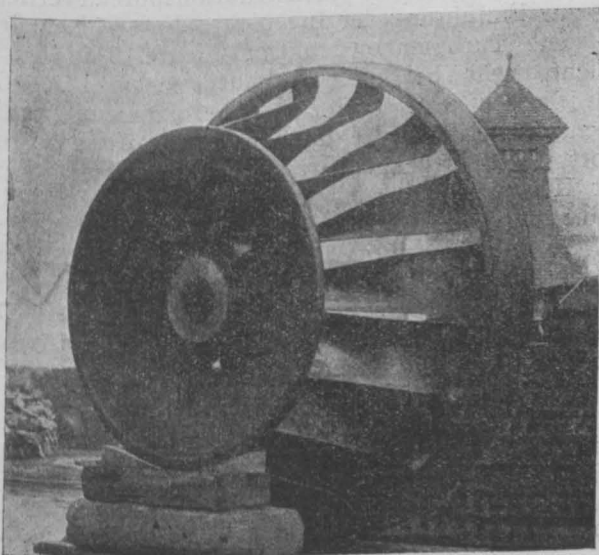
Schnellläufer, nach zweidimensionaler Theorie entworfen für die Maschinenfabrik Vevey.
